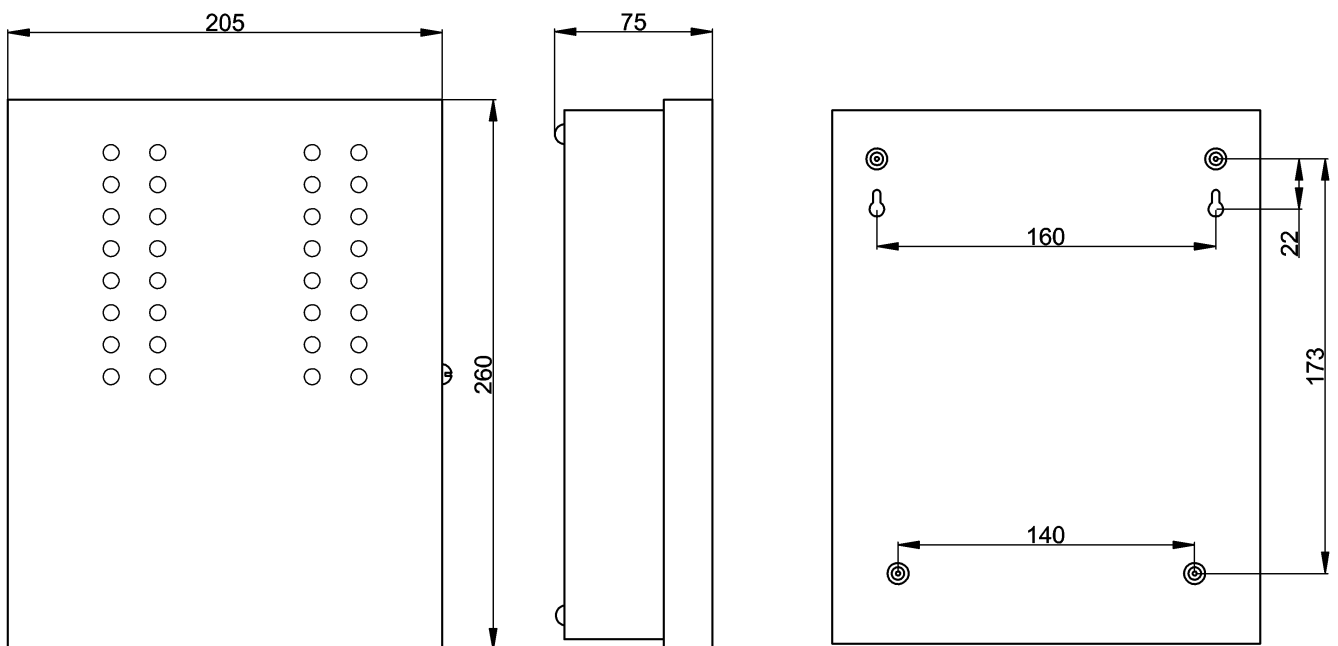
Габаритные и установочные размеры прибора (металлический корпус)
